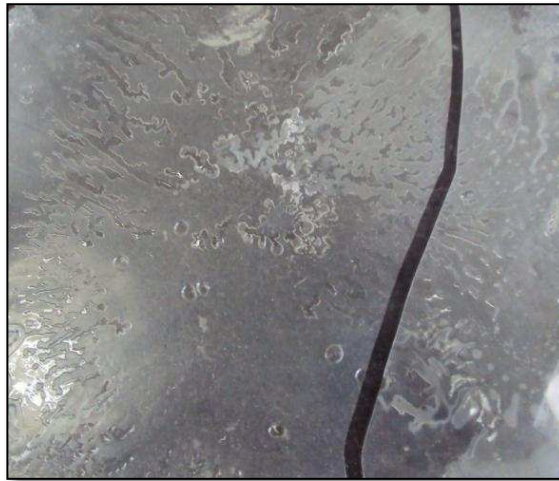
Lámina de ácido poliláctico fracturada al momento de desmoldarse.
